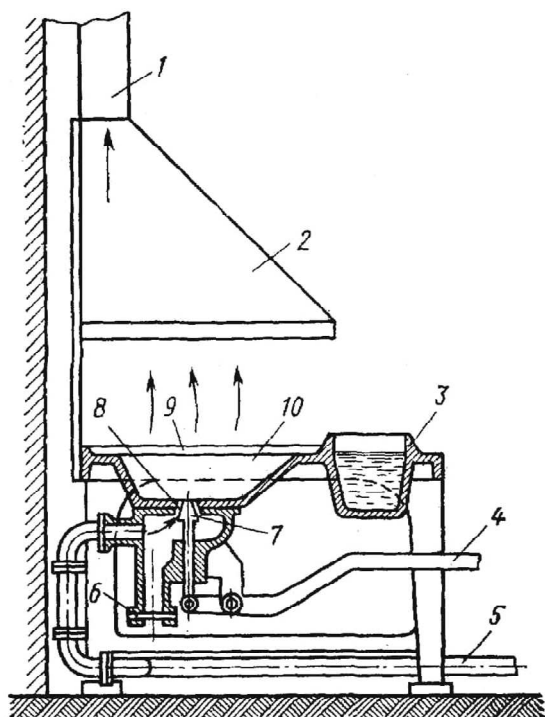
Схема стационарного одноочагового кузнечного горна открытого типа: 1 – вытяжная труба; 2 – зонт; 3 – бачок с водой; 4 – рычаг для регулирования подачи воздуха; 5 – воздухопровод; 6 – заслонка; 7 – клапан; 8 – фурма; 9 – стол; 10 – очаг
